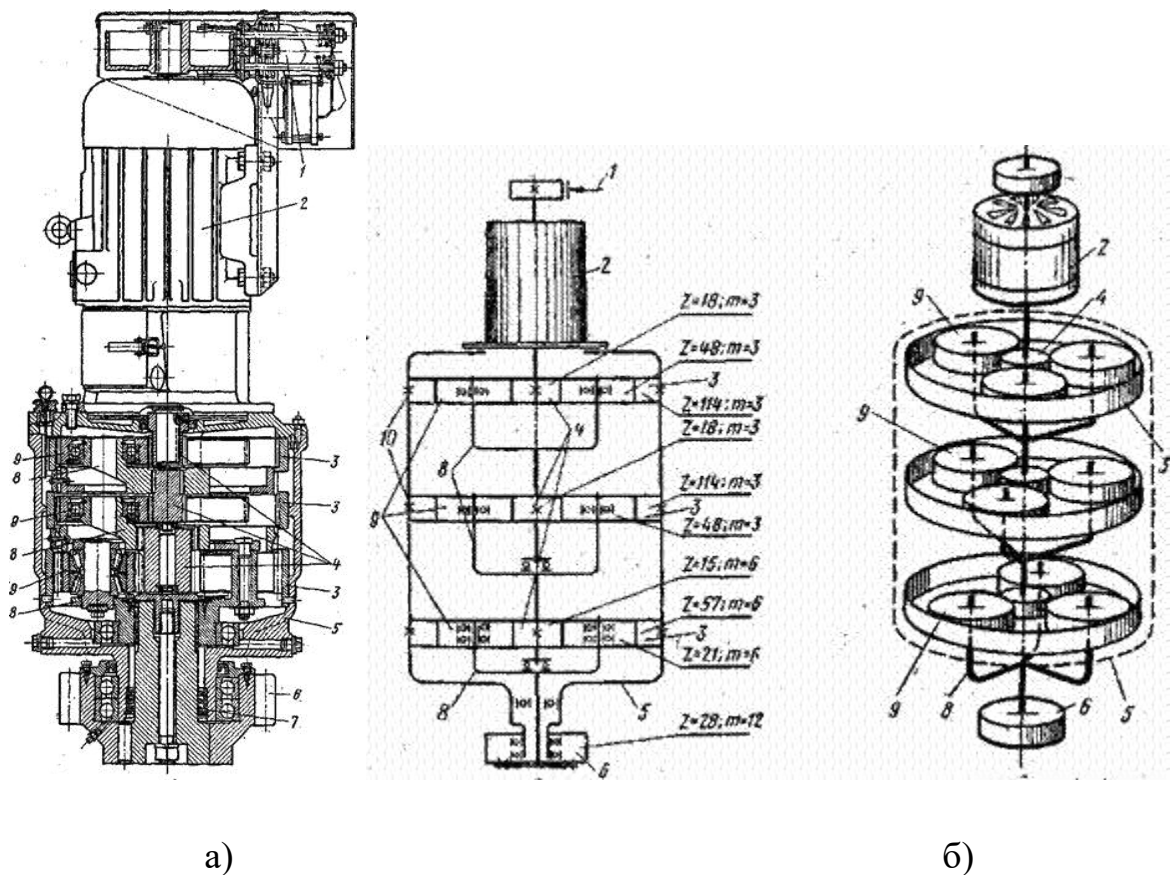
Уніфікований циліндричний механізм повороту: а – розріз редуктора, б – кінематична схема;
